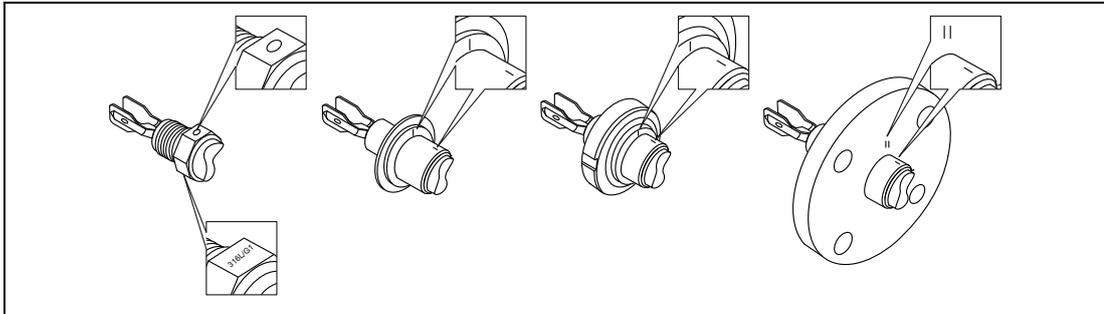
Markierungen für die Ausrichtung der Schwinggabel
